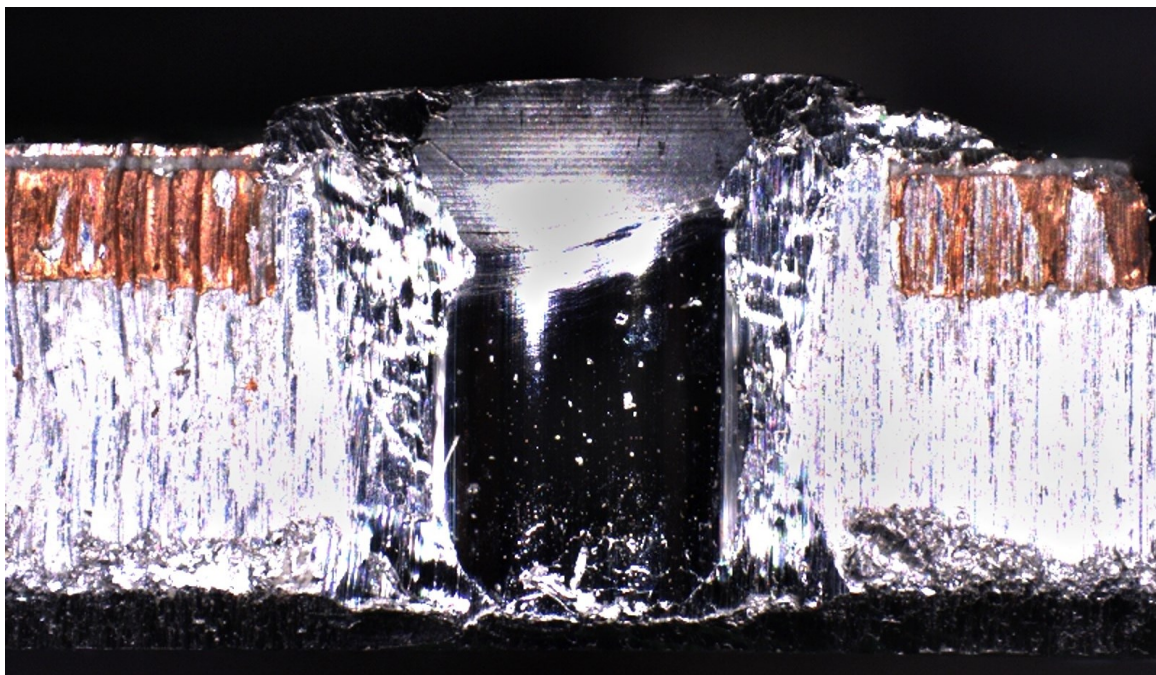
Nýt 2 na vzorku č. 12 – nýt se správným přesahem hlavy přes PCB.
